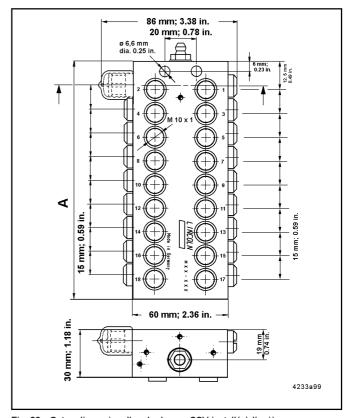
Cotes dimensionelles du doseur SSV installé à l'arrière
